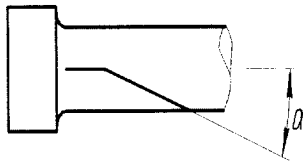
Вид злому закрученого до руйнування зразка
